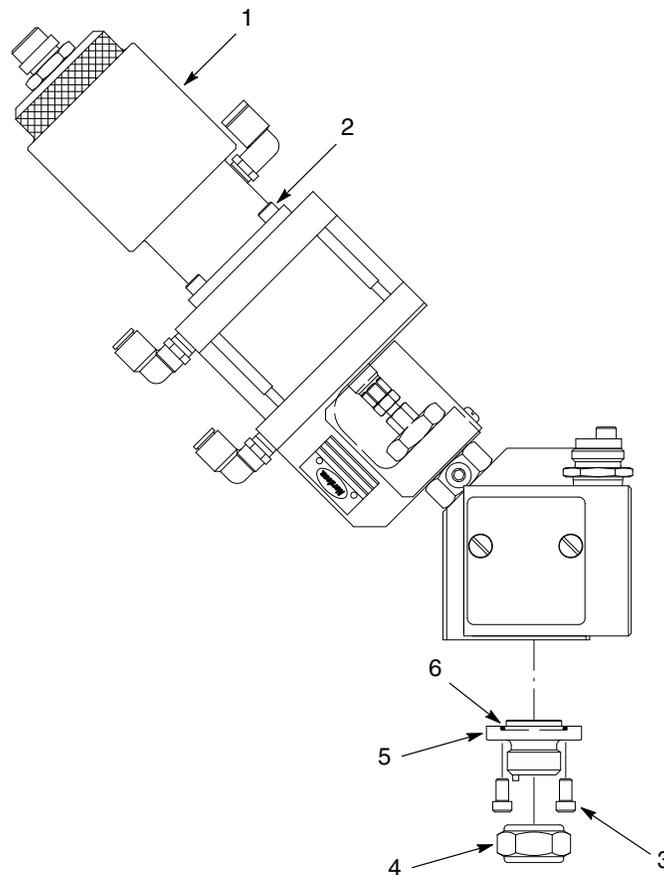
Sätze Federschließbaugruppe und Düsenhalter
